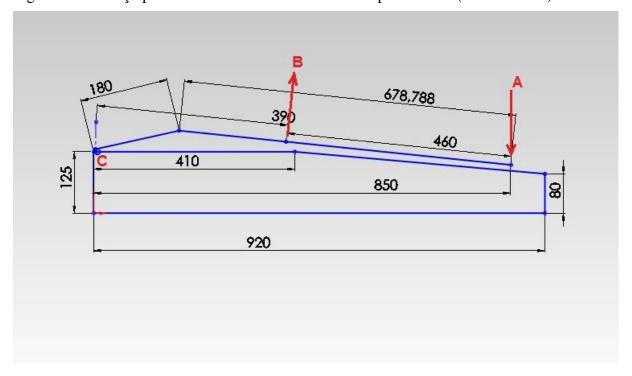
Esboço plano lateral da estrutura do macaco pneumático (cotas em mm).
